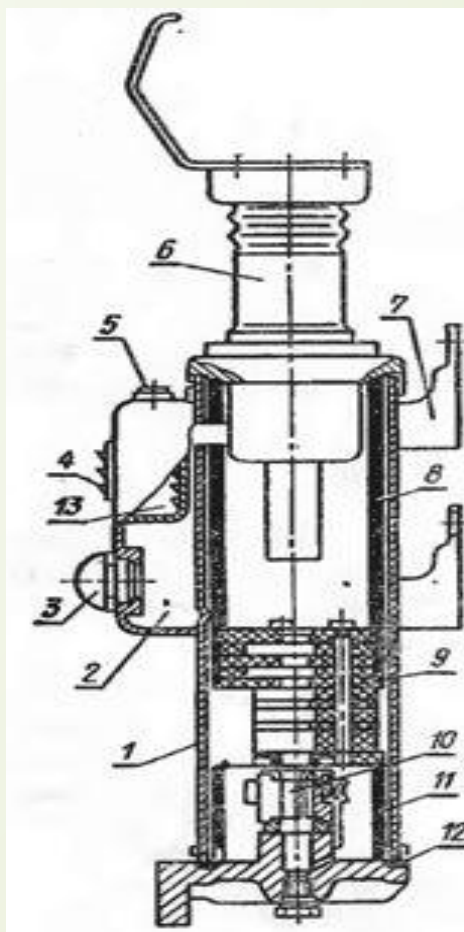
Полюс масляного выключателя ВМГ-10 (1 - сварной цилиндр, 2 - кожух, 3 – масло указатель, 4 - жалюзи, 5 - маслоналивная пробка, 6 - изолятор, 7 - скоба, 8, 11 - изоляционные цилиндры, 9 – дуго-гасительная камера, 10 - розеточный контакт, 12 - уплотнение, 13 - маслоотделитель)
